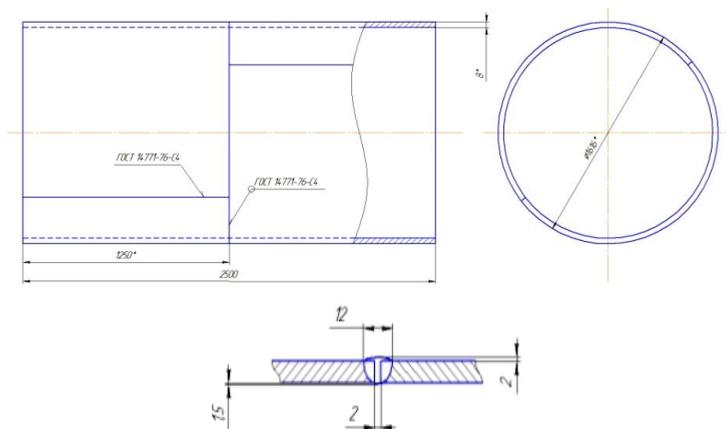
Обечайка резервуара со сварными стыковыми соединениями (односторонние швы С4)
